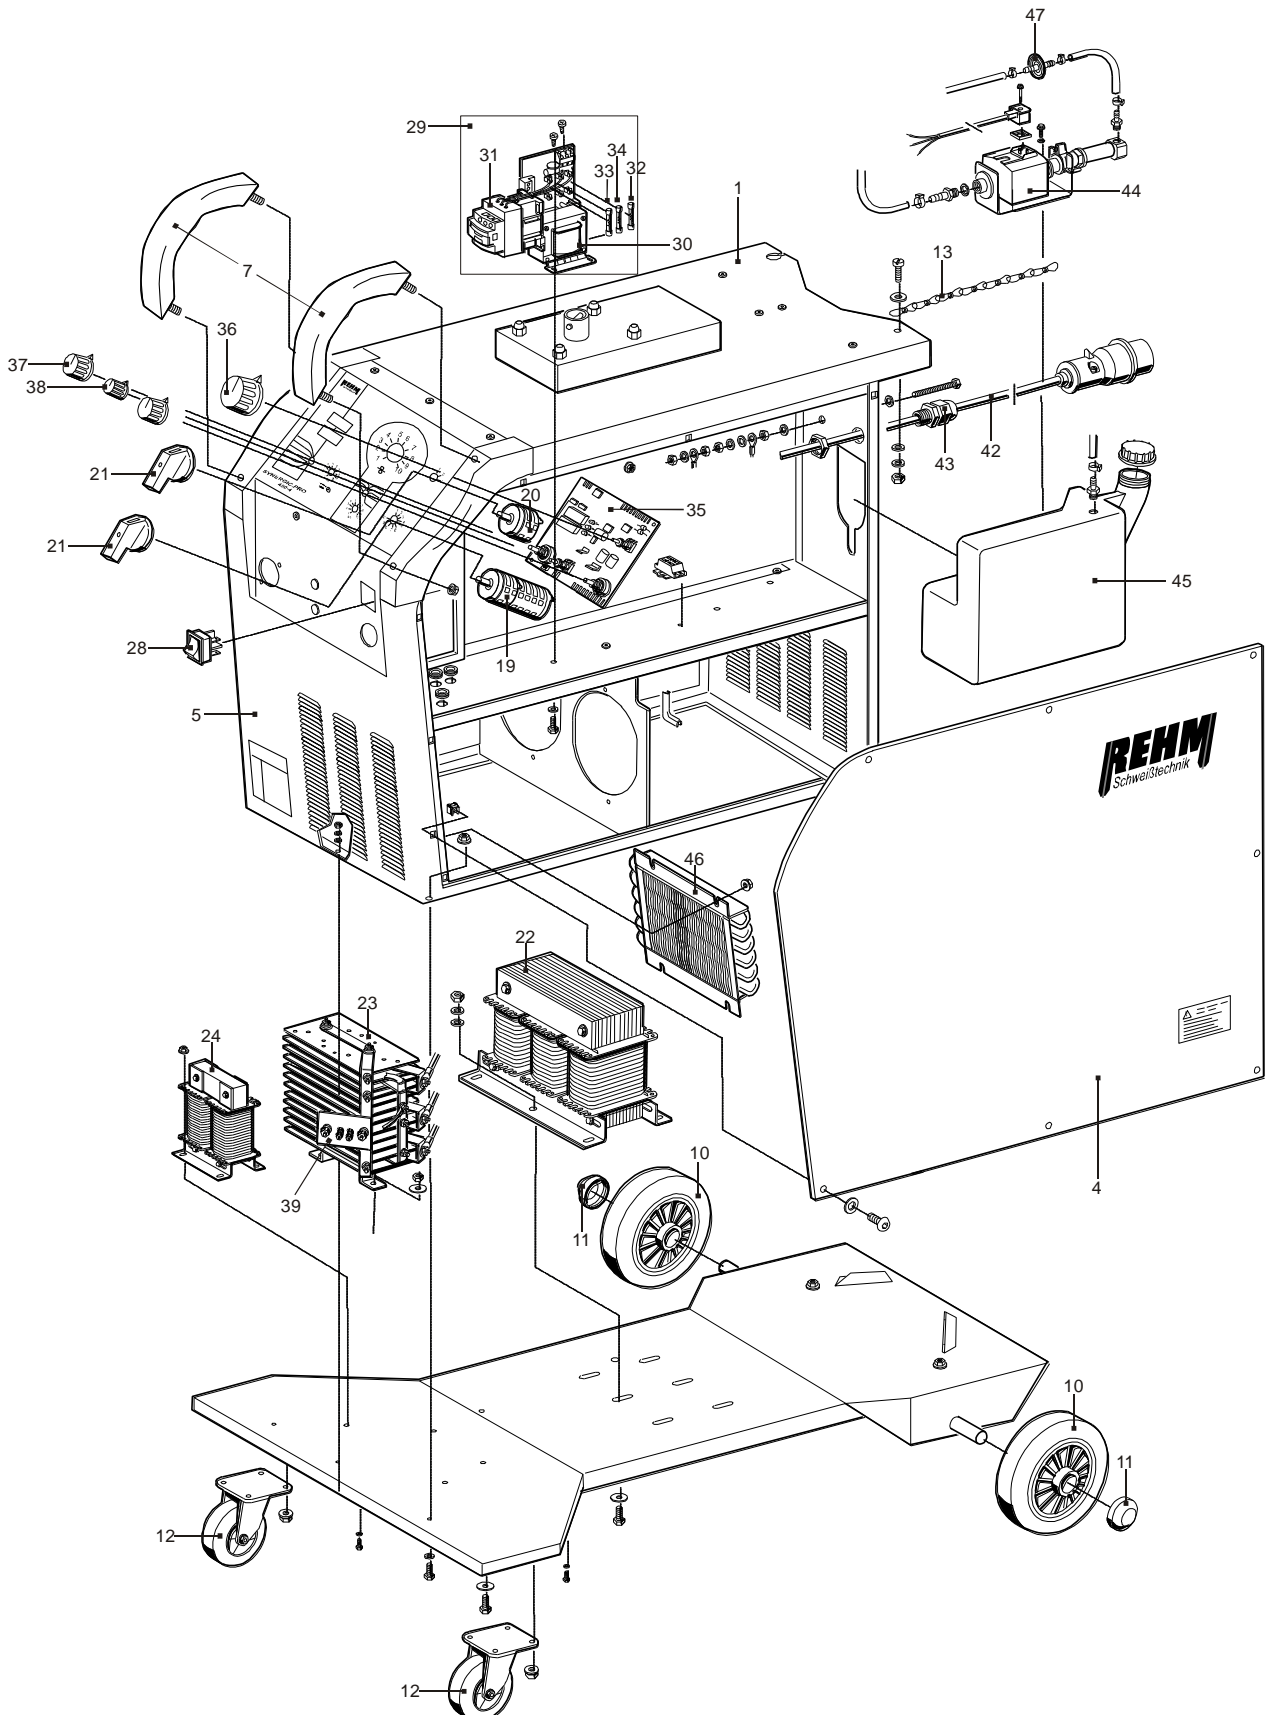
Explosionszeichnung SYNERGIC.PRO² 300-4S – 450-4WS (rechts)
